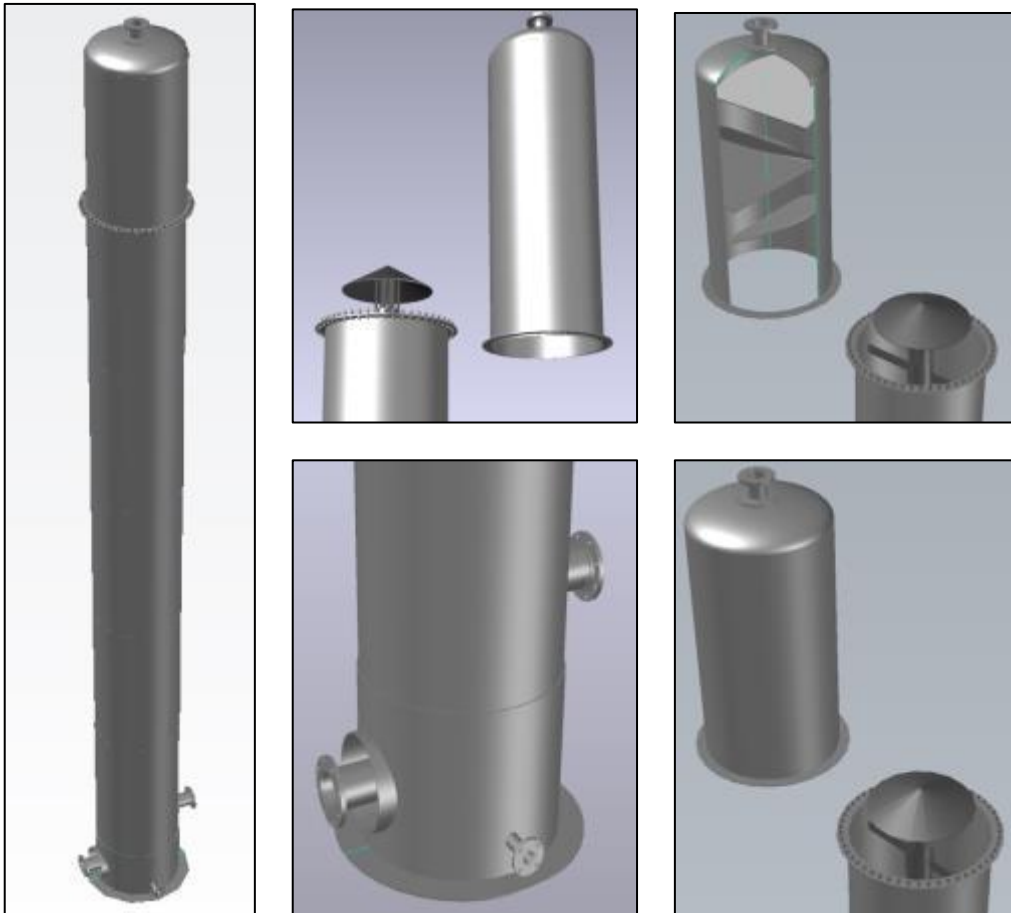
Fotografía Gun Barrel de 500 Bls con Bota de gas integral y bota de gas seccionada. Vista superior difusor
